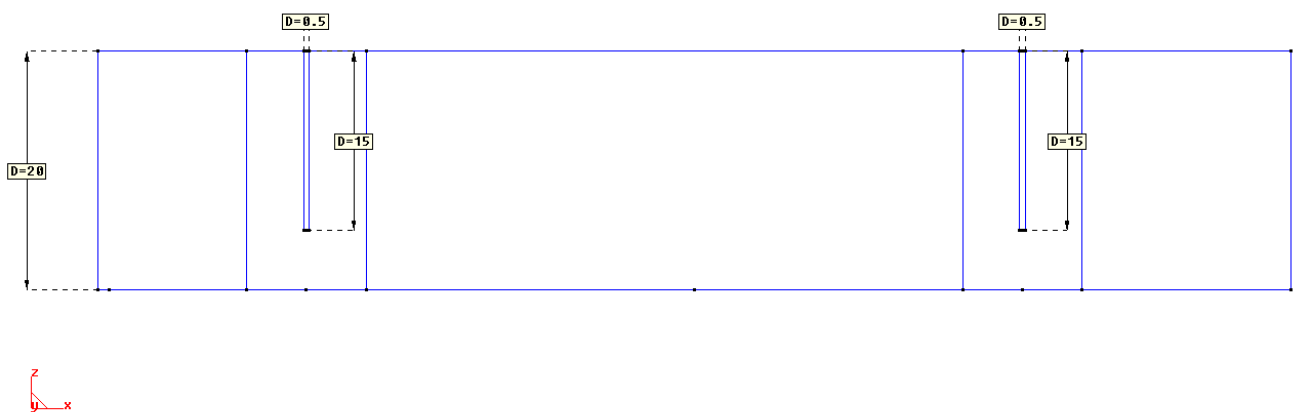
Vista de las cotas en el Plano XZ para $G1$
